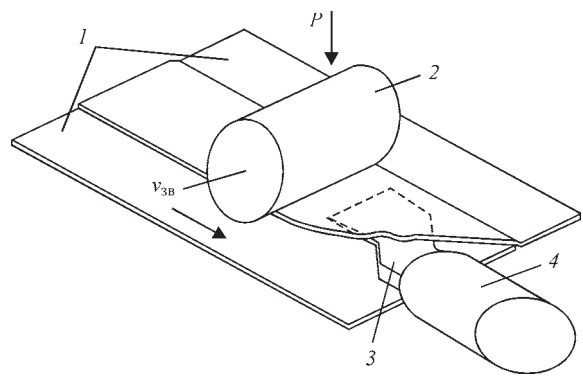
Схема напускного зварювання тканин з ПВХ покриттям за допомогою гарячого повітря: 1 – тканини, що зварюються; 2 – притискний ролик; 3 – сопло для напускного зварювання; 4 – нагрівальний апарат гарячого повітря
